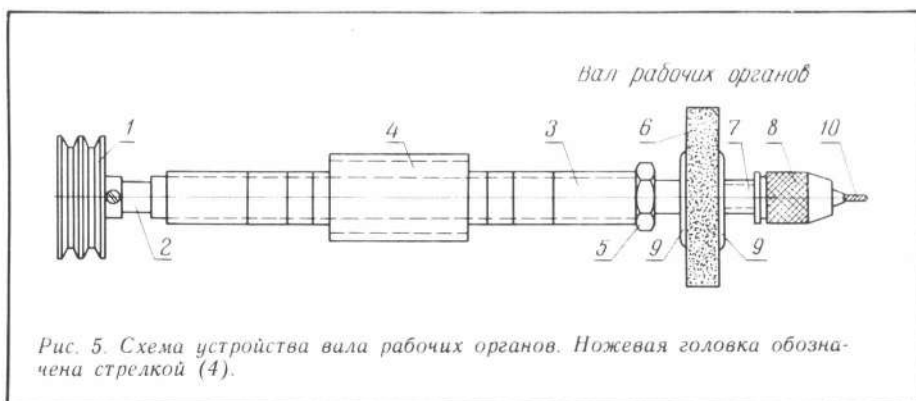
Схема устройства вала рабочих органов. Ножевая головка обозначена стрелкой (4).
